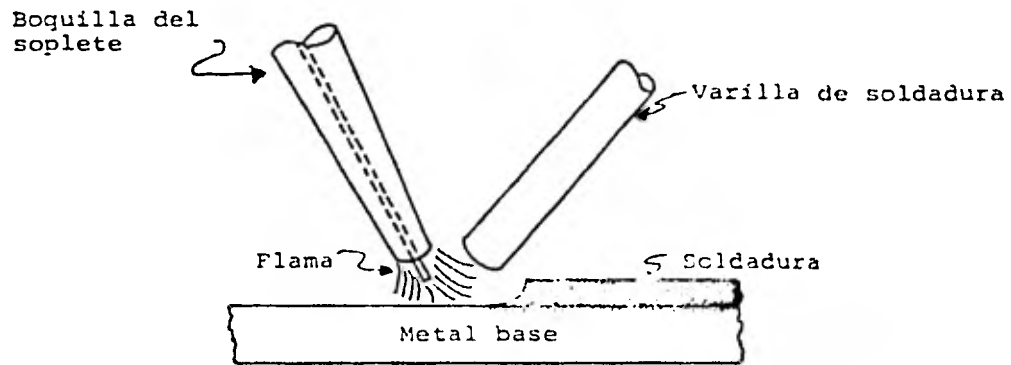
12 Soldadura Oxi-acetileno
